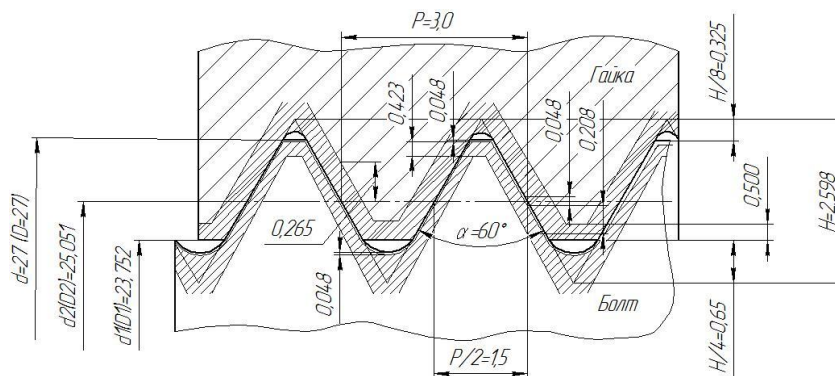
Схема расположения полей допусков для резьбового соединения $M27-6H/5g6g$ (резьба с крупным шагом 3,0).
